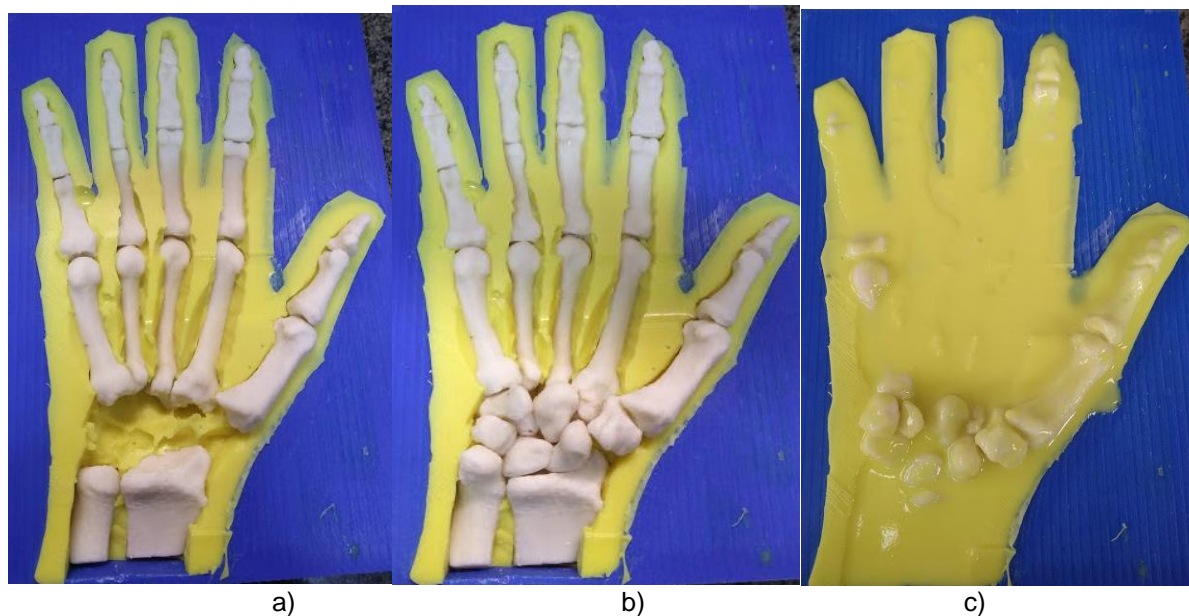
Lado A com mistura de poliuretano e molde ósseo posicionado
